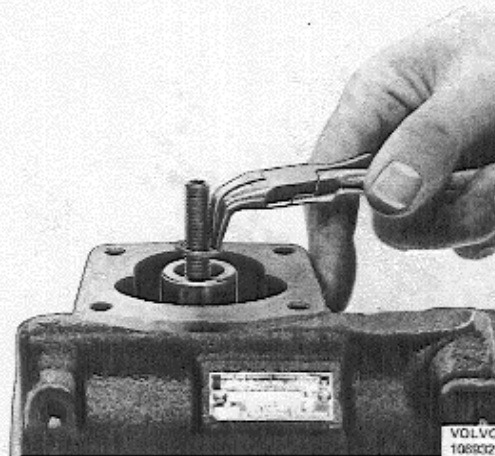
Ausfedern des Sicherungsringes, Einstellschraube
